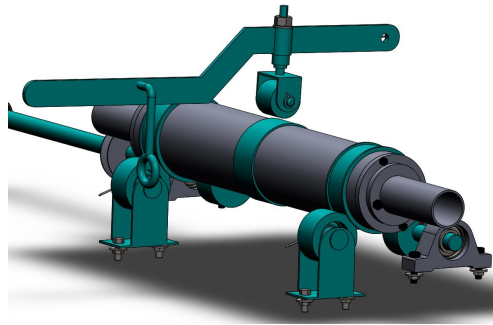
Apoyo del molde en rodets con palanca superior.
